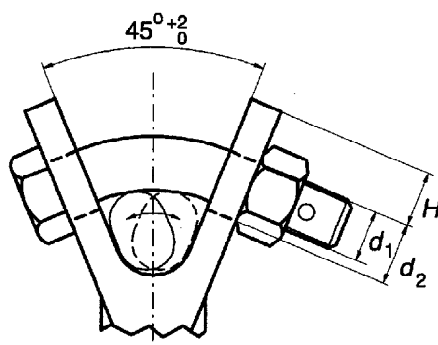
Dimensions des accrochages de type chape en Y et des calibres
